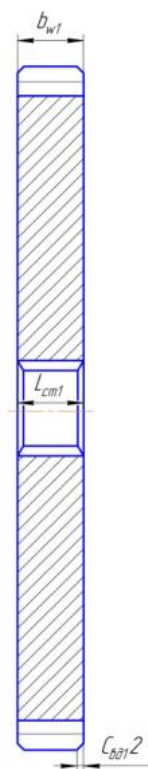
Ведущая шестерня заднего колесного редуктора
